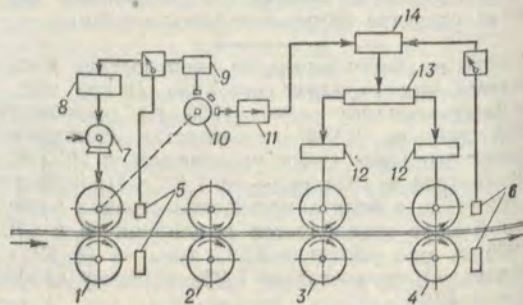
Схема автоматического контроля и регулирования толщины полосы, прокатываемой на непрерывном стане: 1, 2, 3, 4 — рабочие валки четырех клетей; 5, 6 — лучевые микрометры; 7 — двигатель нажимного механизма; 8 — усилитель; 9 — запоминающий барабан электронно-вычислительного устройства, вращающийся синхронно с валками первой клетки; 10 — усилитель; 11 — регулятор натяжения; 12, 13 — приводы третьей и четвертой клетей; 14 — электронно-вычислительное устройство.
